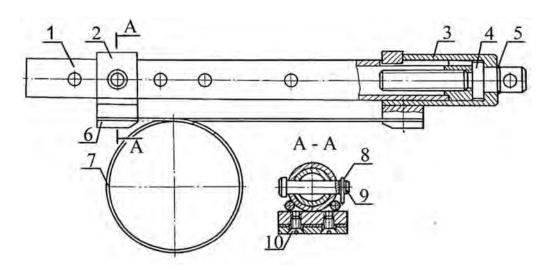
Прибор для обжатия фторопластовых шайб: I — направляющая; 2 — корпус; 3 — ползун; 4, 10 — винты; 5 — стопорное кольцо; 6 — планка; 7 — лента; 8 — кольцо; 9 — ось
